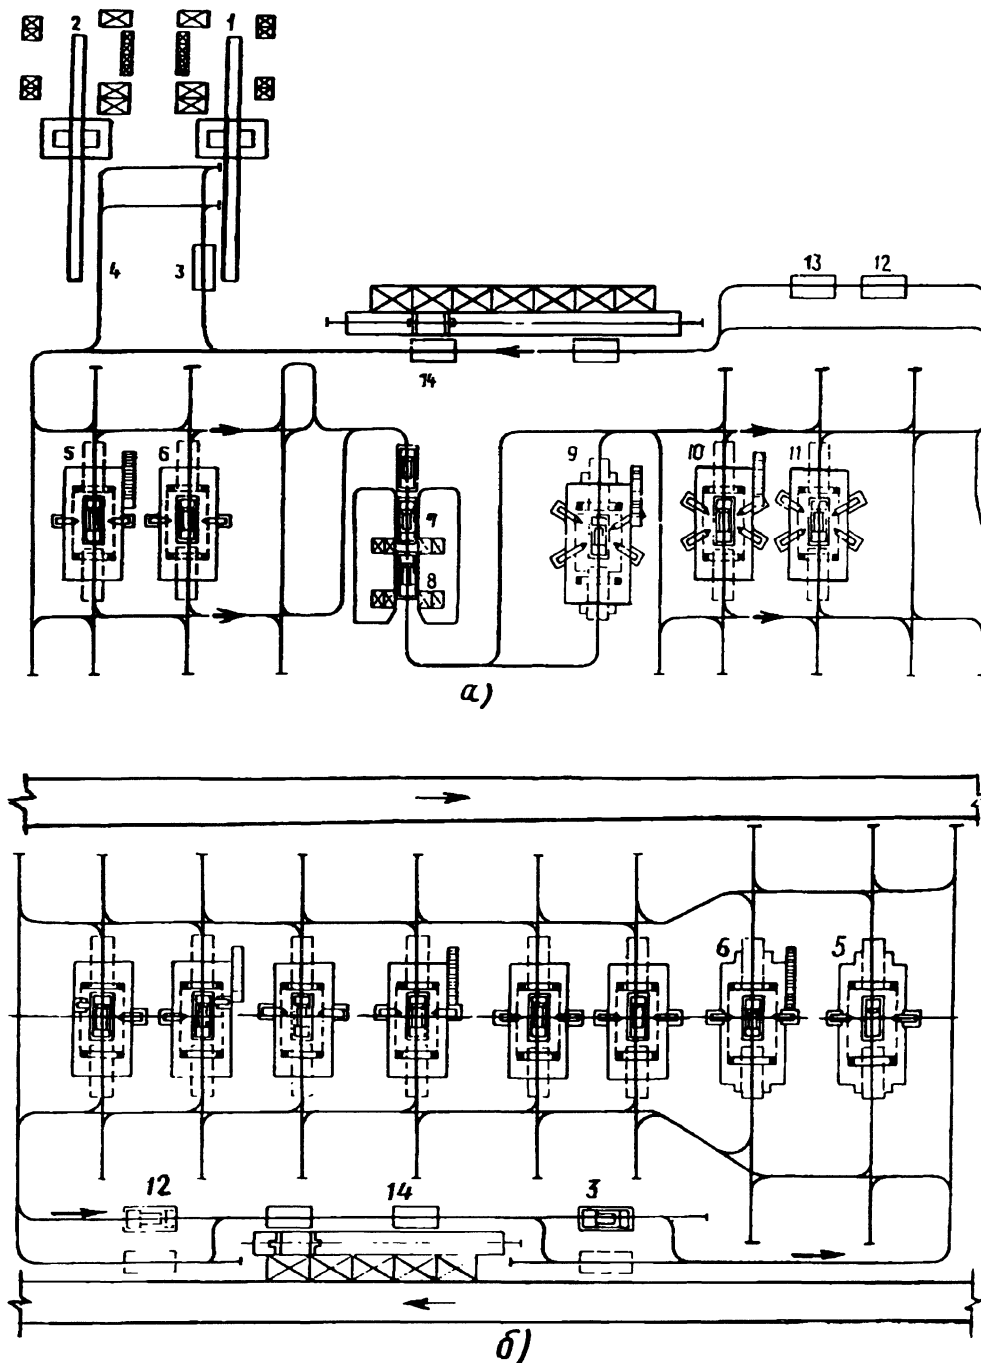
Гибкая производственная система типа Робогейт для сварки тонколистовых конструкций — кузовов легковых автомобилей:
